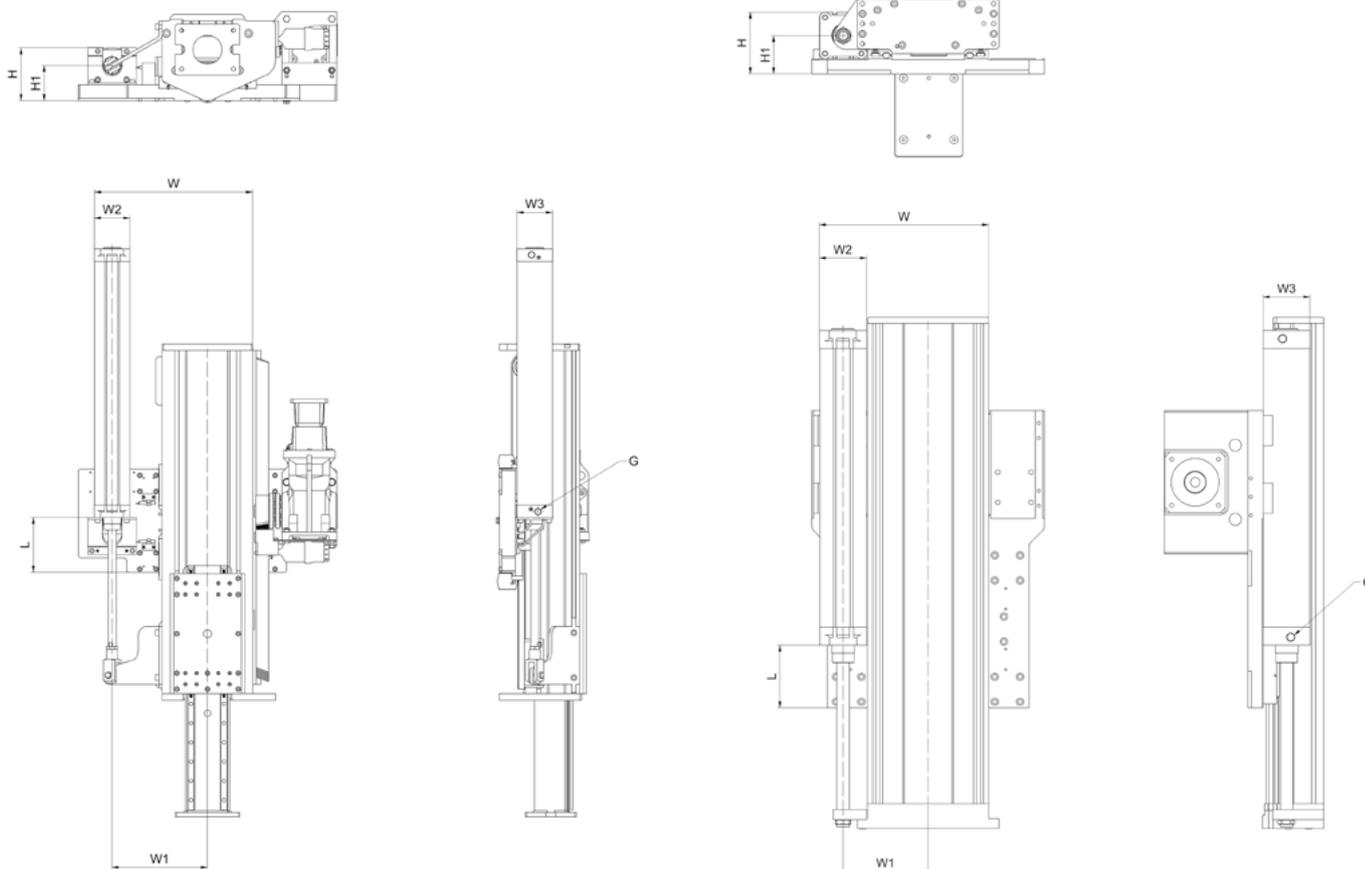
AXDL240A und AXS280TV mit Ausgleichszylinder
